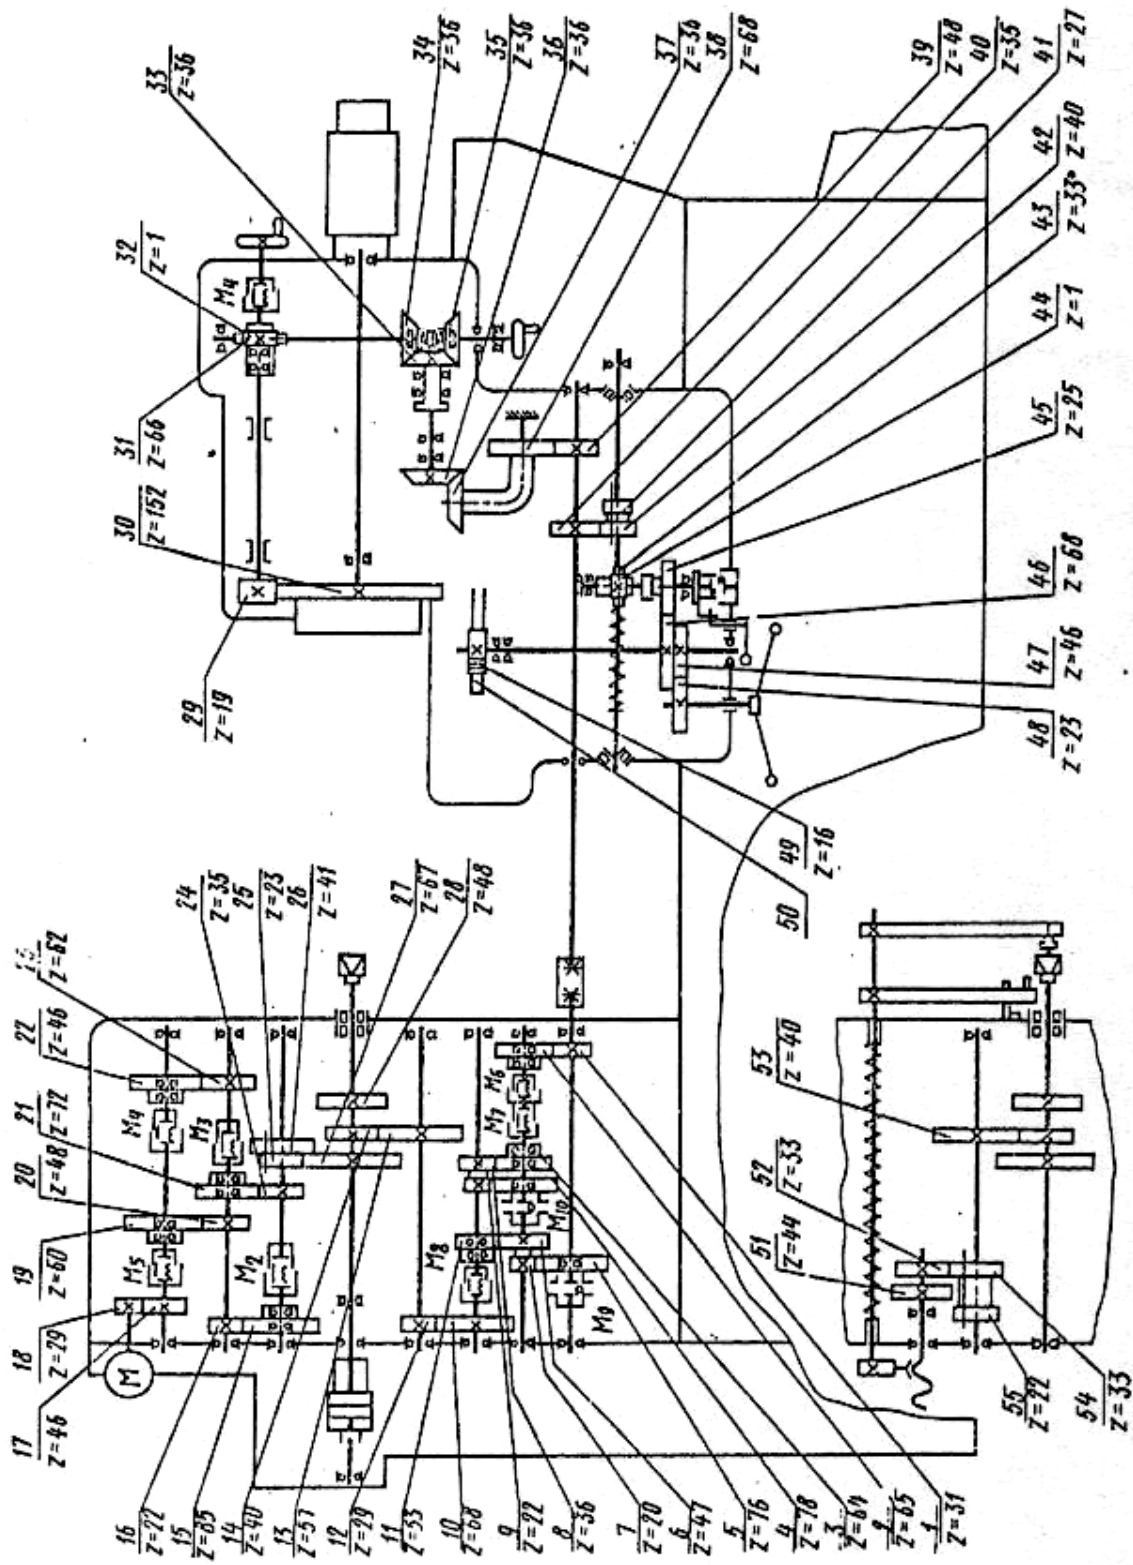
Кінематична схема токарно-револьверного верстага модної 1К341
